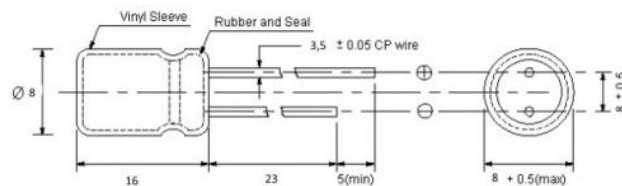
Габаритні розміри конденсатора типу ЕСАР
